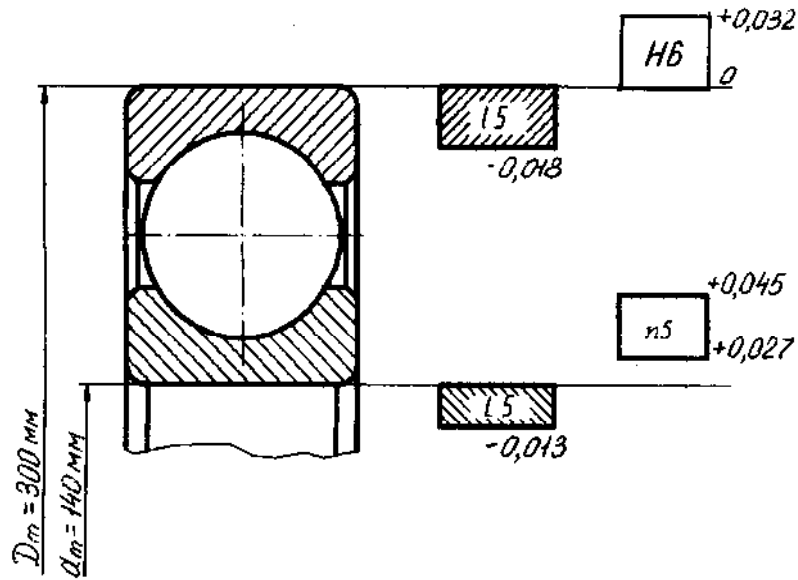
Схема розташування полів допусків кілець підшипника, вала та отвору корпуса
